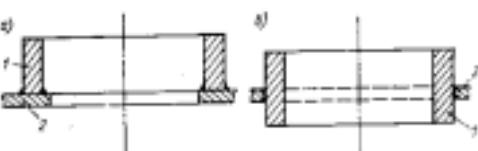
Конструкция соединения комингса вентиляционной шахты с палубным стрингером:
